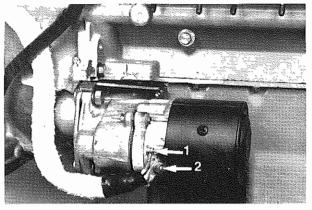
Cavi motorino d'avviamento (C. aut.) Starter motor cables (Autom. transmission)
